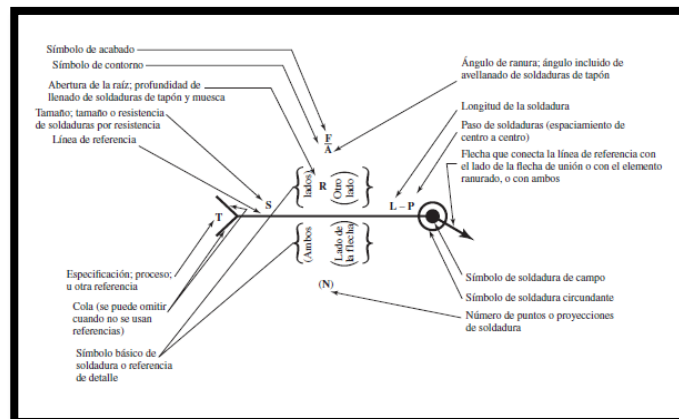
Representación simbólica de soldadura estándar AWS con la ubicación de los elementos del símbolo.
